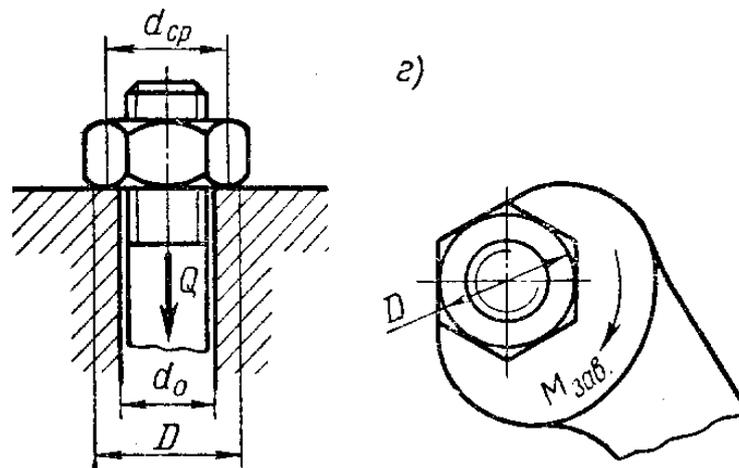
До питання визначення зовнішнього діаметра опорної поверхні гайки
